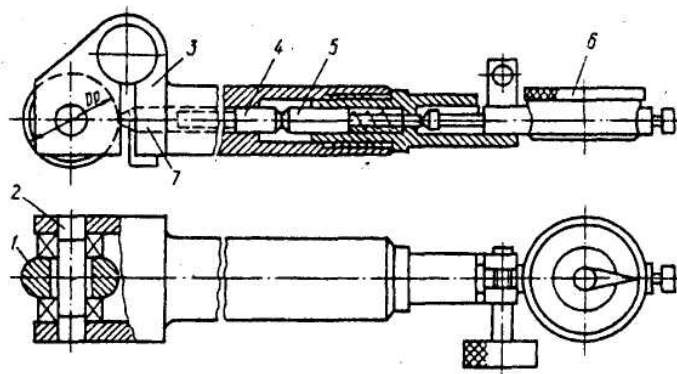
Пристрій для обкатування зовнішніх циліндричних поверхонь: 1 – ролик; 2 – вісь; 3 - корпус; 4 – штовхач; 5 – стрижень; 6 – індикатор годинникового типу; 7 - упор
